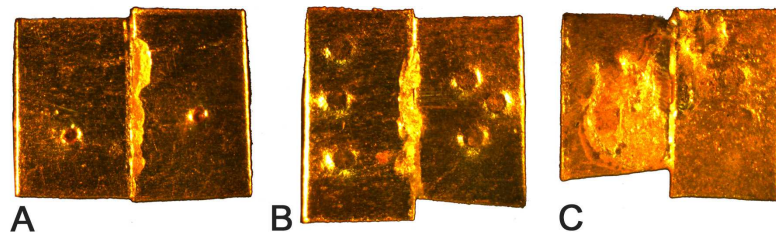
Soldaduras por aleación soldante. Las imágenes A y B muestran rebabas de fusión en la zona de soldadura debido al exceso de material soldante, la imagen C muestra un ejemplo de soldadura libre de rebabas.
